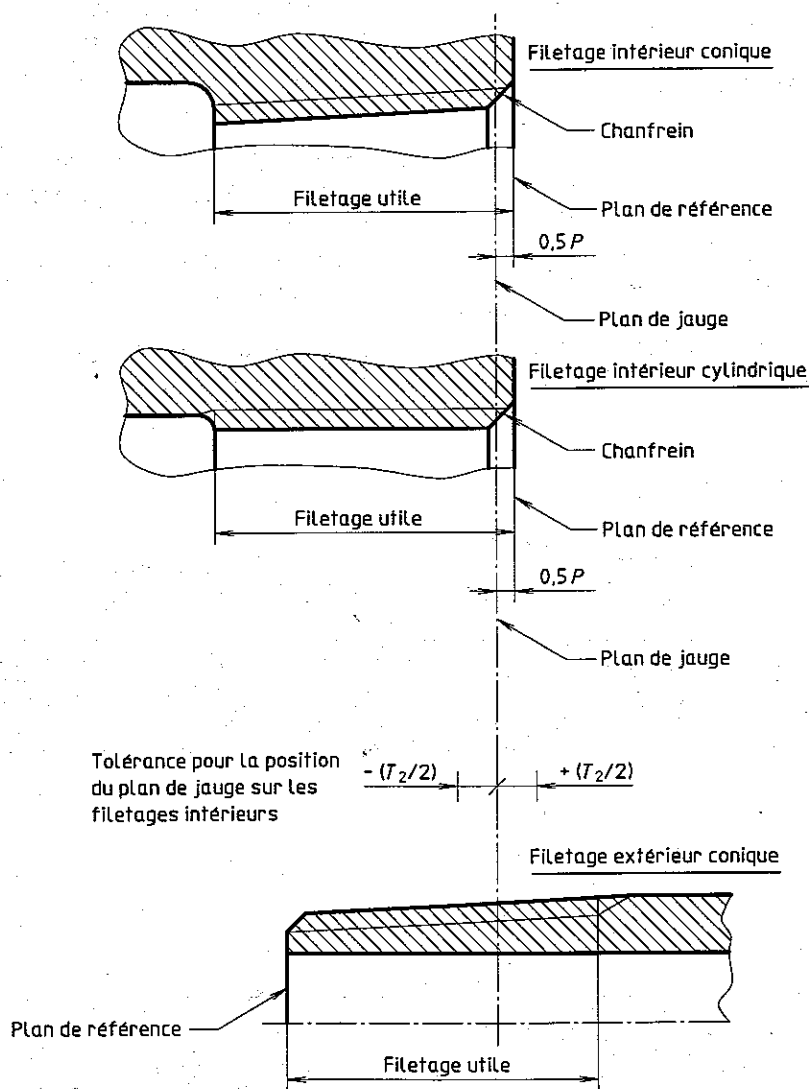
Filetages intérieur et extérieur de tuyauterie (position du plan de jauge, plan de référence, filetage utile)
